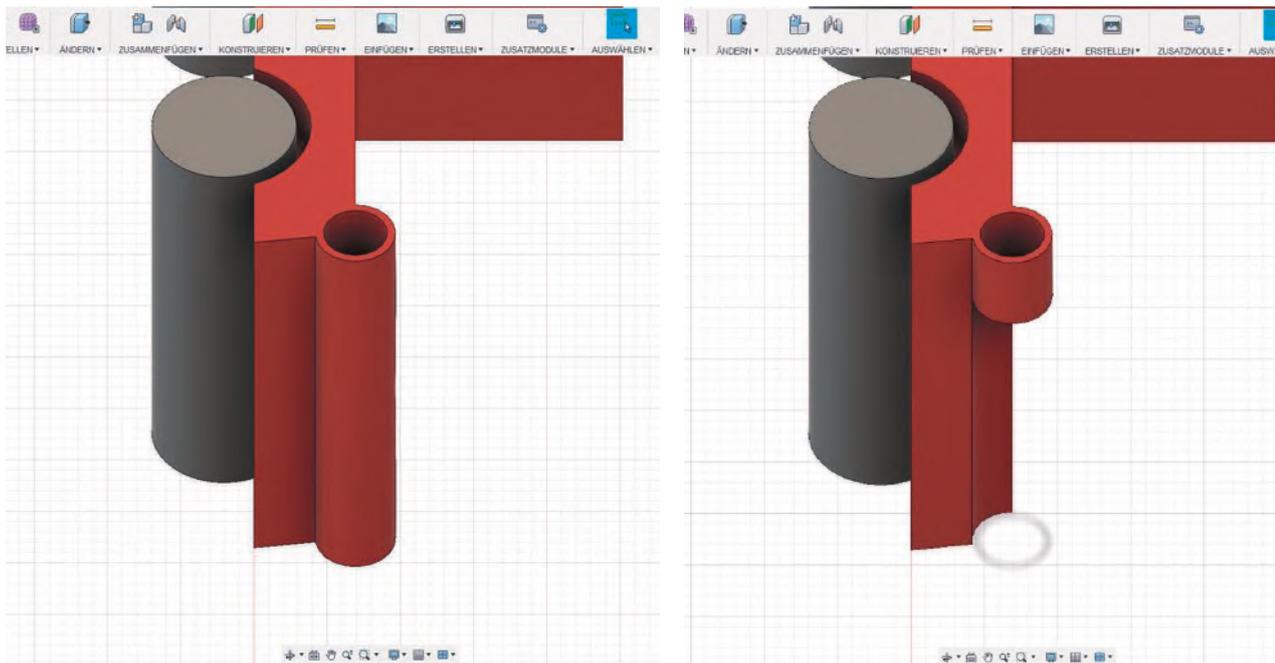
Projet « Camion avec charnière » - Extrusion et découpe des solides
